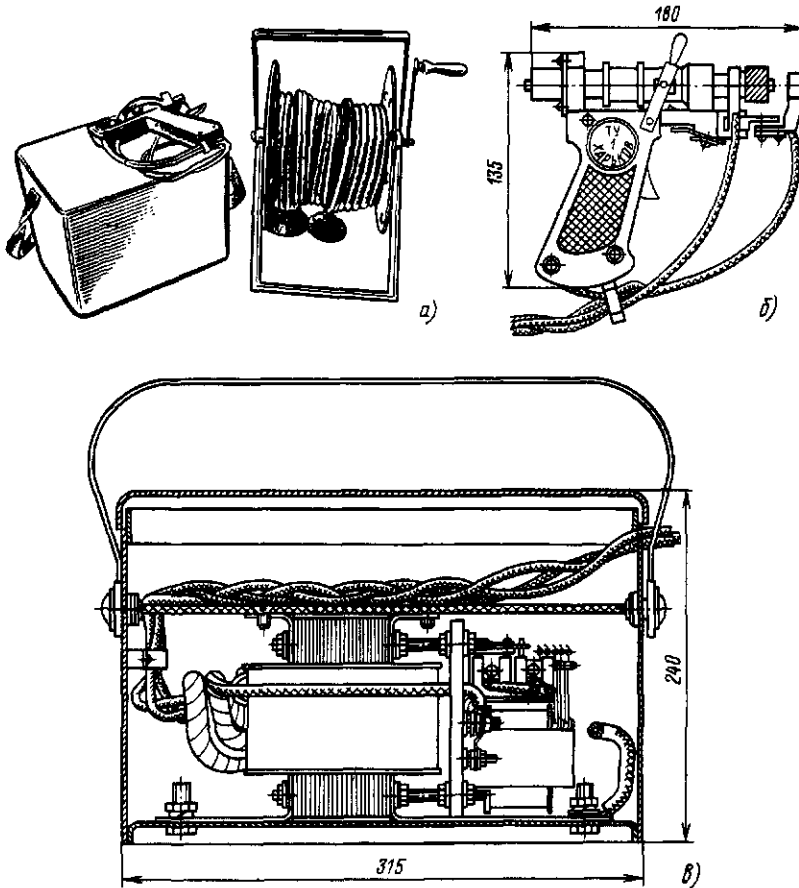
Аппарат для сварки одножильных проводов
